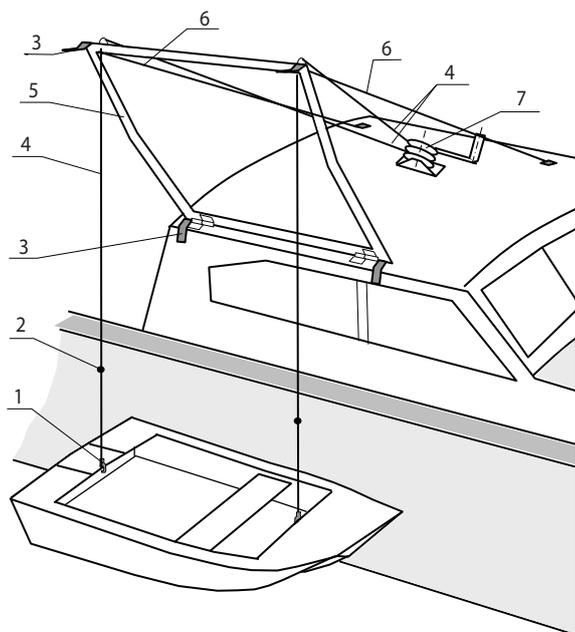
Приспособление для подъема бортовой лодки на крышу рубки
